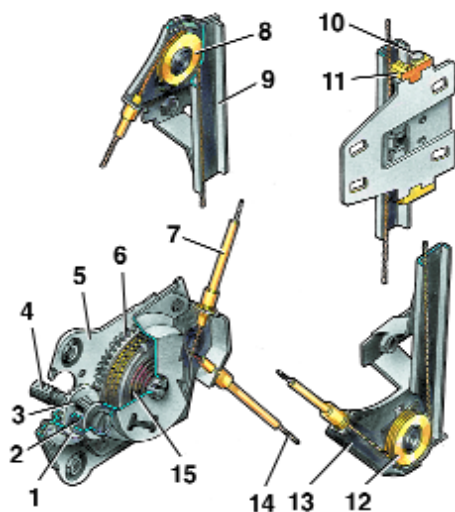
Стеклоподъемник передней двери: 1 – чашка тормоза; 2 – пружина тормоза; 3 – шестерня; 4 – валик; 5 – корпус стеклоподъемника; 6 – барабан; 7 – оболочка троса; 8 – верхний ролик стеклоподъемника; 9 – направляющая стеклоподъемника; 10 – шарнир сухаря; 11 – сухарь ползуна; 12 – нижний ролик стеклоподъемника; 13 – кронштейн ролика; 14 – трос стеклоподъемника; 15 – пружина барабана
